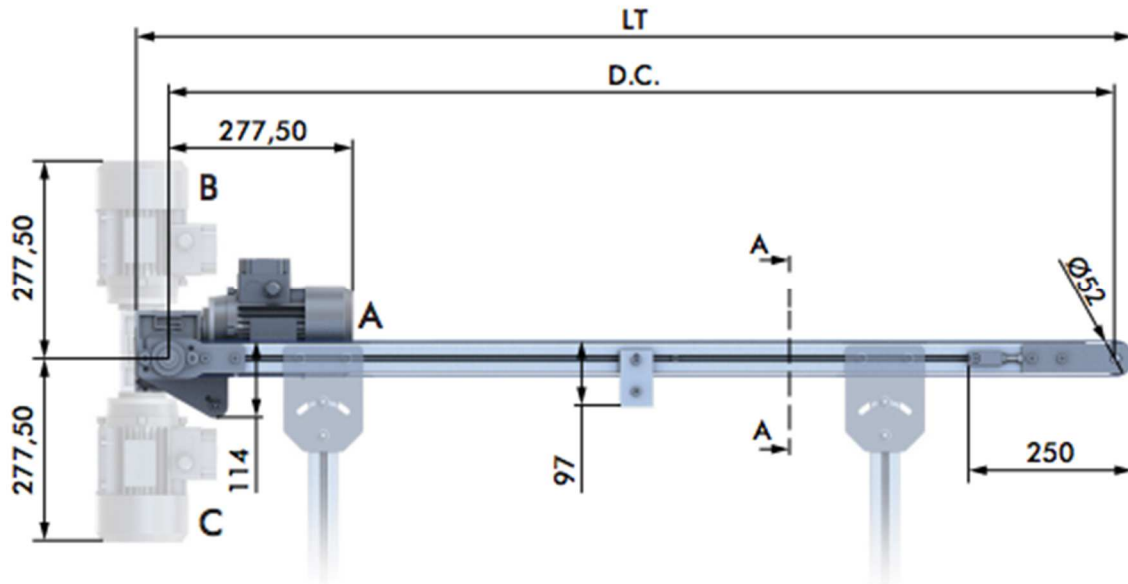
Distintas configuraciones del motor en las cintas transportadoras. Fuente: Camprodón
